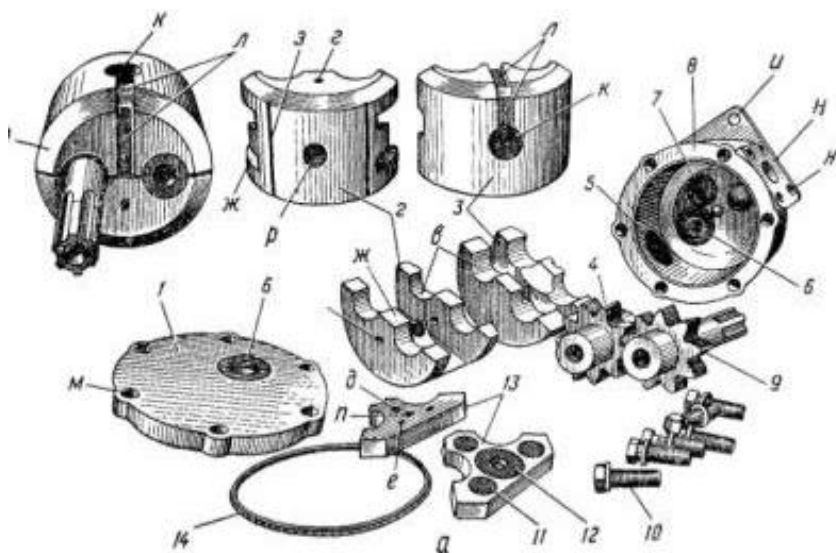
Шестеренный круглый насос типа НШ-100: 1 — крышка насоса; 2 — поджимная (подвижная) обойма; 3 — подшипниковая обойма; 4 — шестерня ведомая; 5 — манжета радиального поджима; 6 — манжета диаметром 39 мм; 7 — центрирующая втулка; 8 — корпус; 9 — шестерня ведущая; 10 — болты с пружинными шайбами для крепления крышки насоса; 11 — манжета диаметром 16 мм; 12 — манжета диаметром 29 мм, 13 — пластики-замыкатели; 14 — уплотнительное кольцо крышки насоса; в — выточки под цапфы шестерен; г — отверстие диаметром 6 мм; д — расточка диаметром 6 мм и глубиной 2 мм; е — косые отверстия; ж — пазы под пластики-замыкатели; з — треугольные пазы; и — отверстие для крепления насоса; к — отверстие всасывающее (входное); л — канавка для отвода утечек; м — отверстия под болты 10; н — обработанные плоскости для крепления присоединительной арматуры; о — фаска широкая; п — отверстие диаметром 6 мм; р — отверстие нагнетательное.
